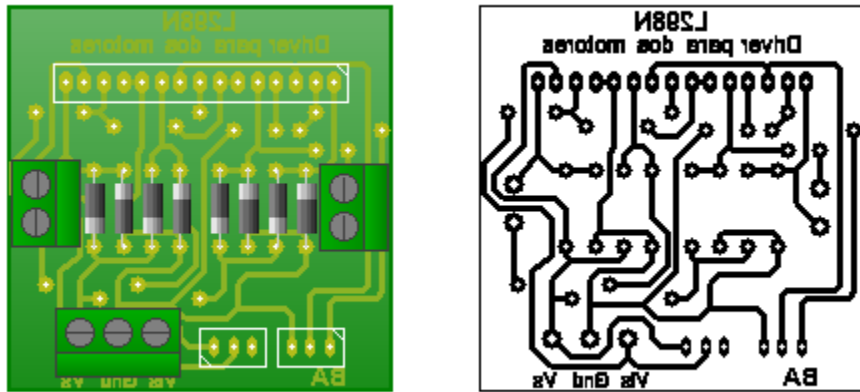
Rutado del puente h-l298b, PCB Wizard.
